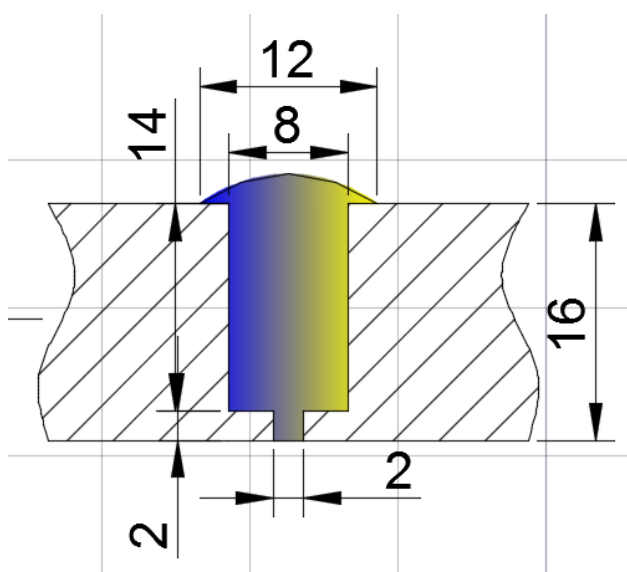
сечение сварного стыка труб Ø1220 мм и толщиной стенки 16 мм, со сварным швом, выполненным в щелевую разделку.
